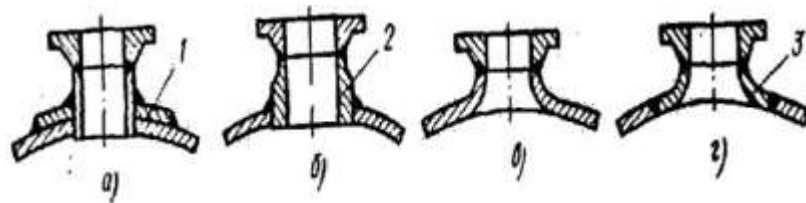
Способы соединения люков и штуцеров с корпусами аппаратов
